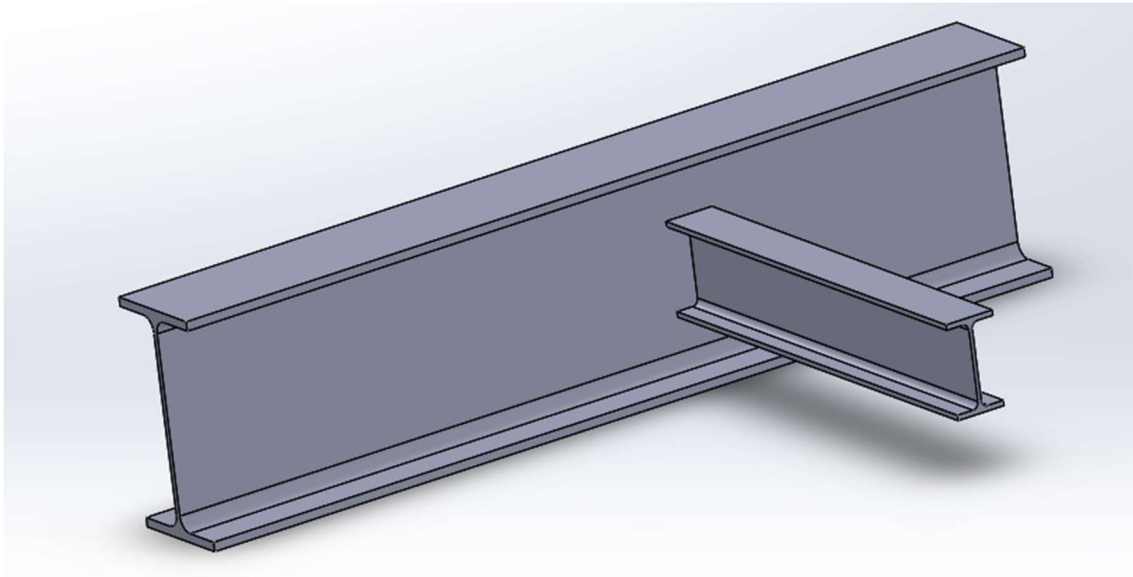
Soldadura travesaño 2 con larguero.
